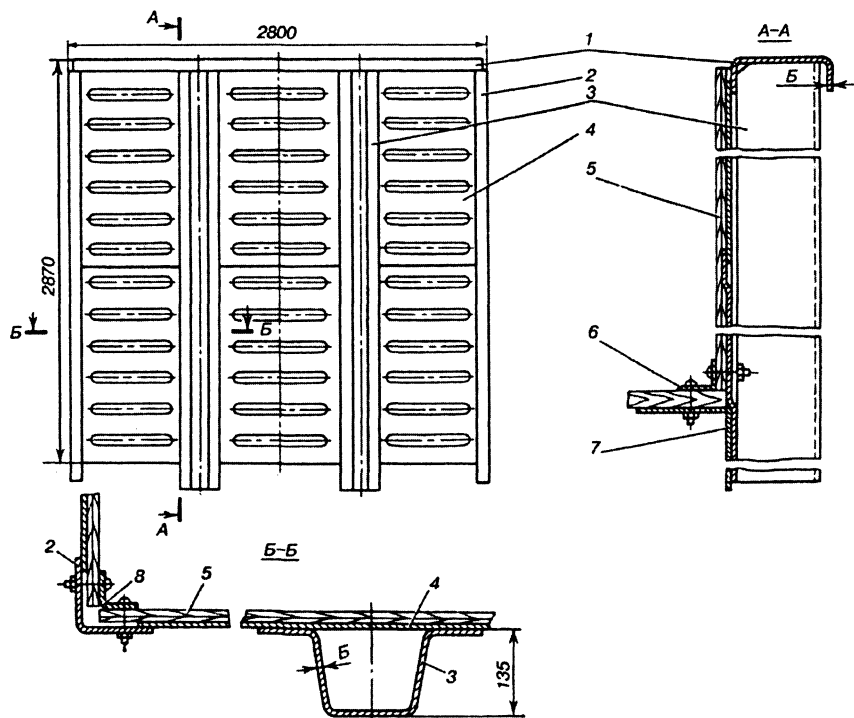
Торцовая стена кузова универсального крытого вагона
